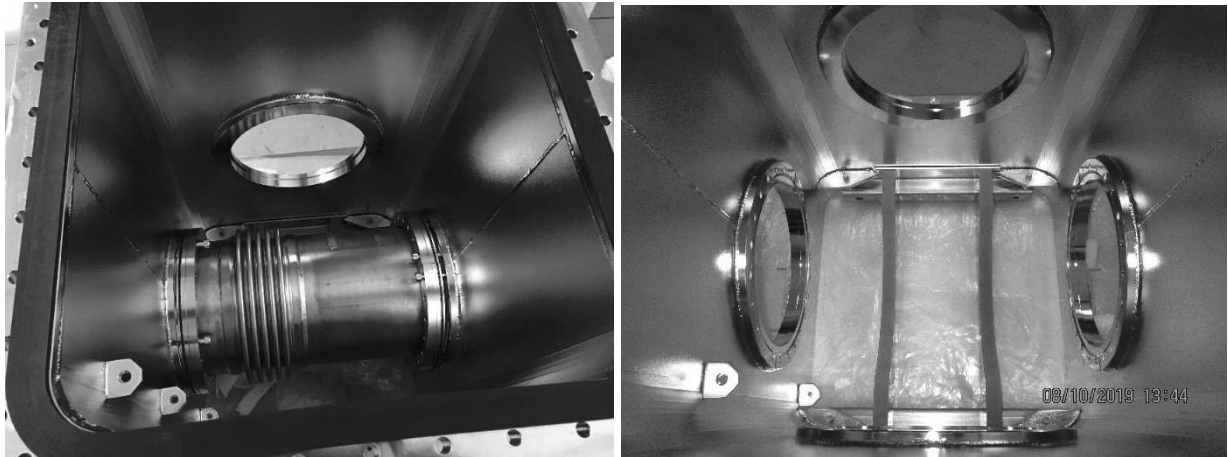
Montagezustand oberer und unterer Flansch geöffnet: mit (links) und ohne (rechts) Helium-Dummy-Rohr im Helium-Behälter
